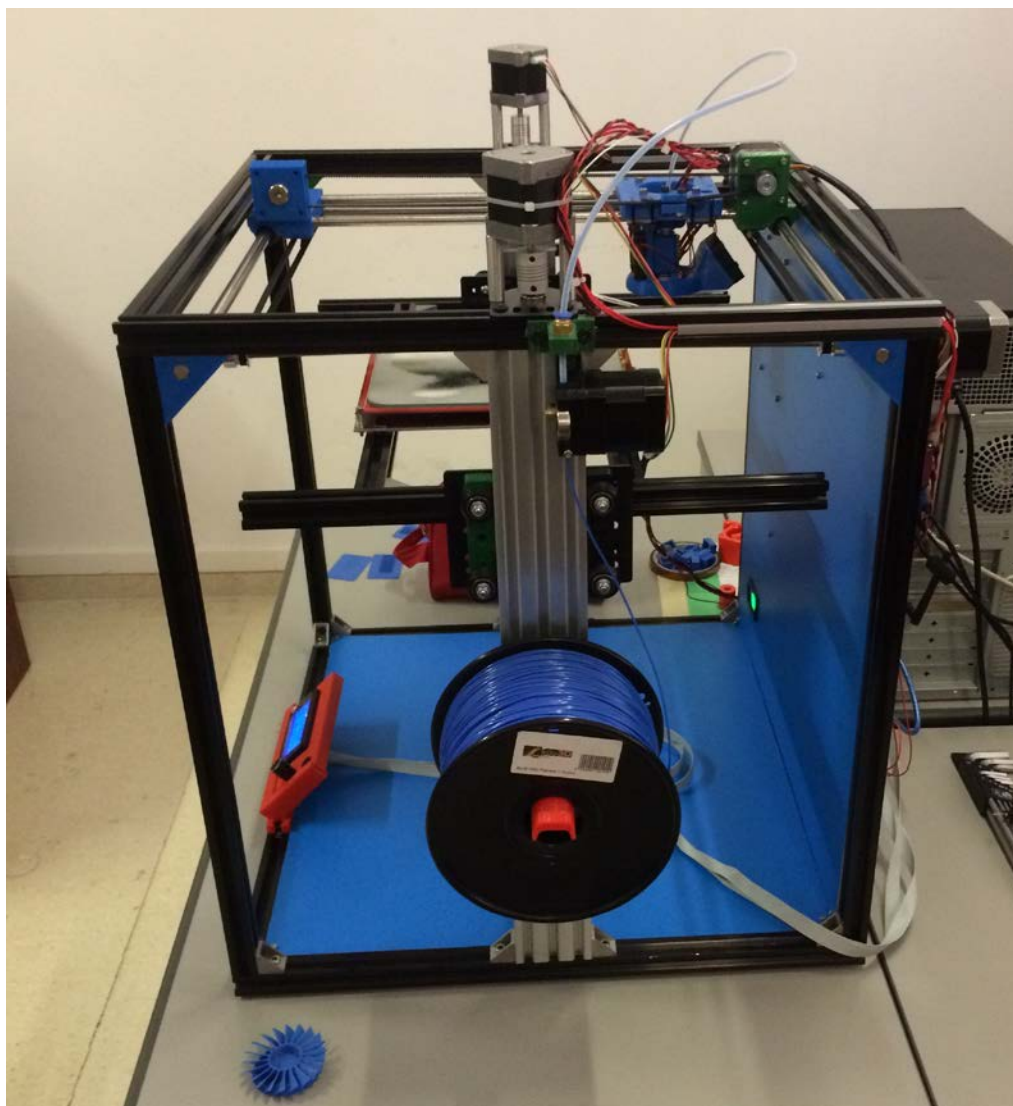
Detalle bobina, extrusor y cableado
